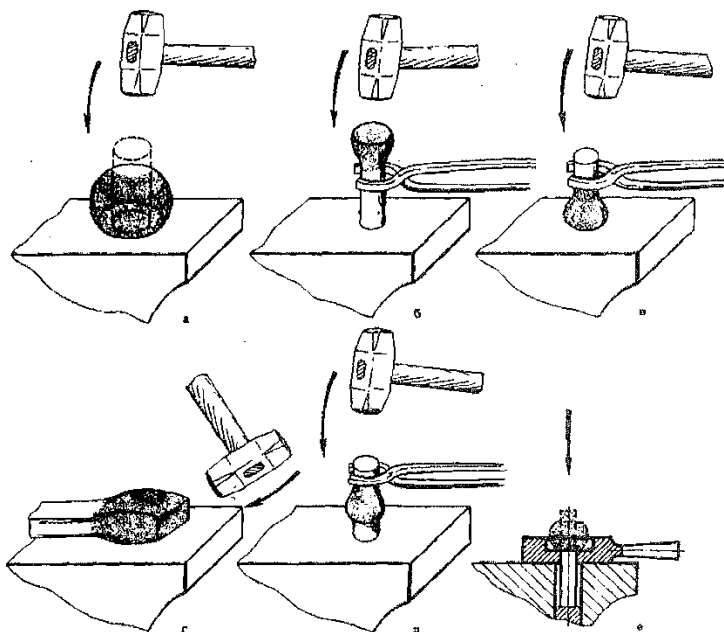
Осадка и высадка: *а* – осадка цилиндрической заготовки; *б, в* – высадка верхней и нижней частей заготовки; *г* – высадка конца плоской заготовки; *д* – высадка средней части заготовки; *е* – высадка головки в гвоздильни.
